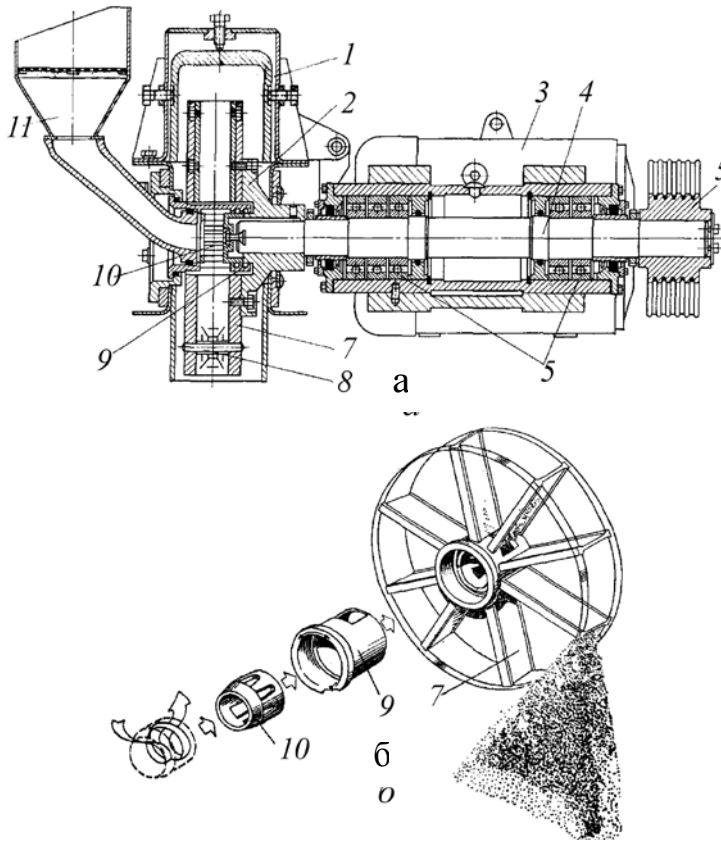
Дробометальний апарат: а - конструкція; б - принцип дії; 1 - кожух; 2 - ротор; 3 - електродвигун приводу; 4 - вал; 5 - шків; 6 - підшипники; 7 - лопать; 8 - штифт; 9 - розподільна коробка; 10 - розподільник дробу; 11 - завантажувальна воронка.
